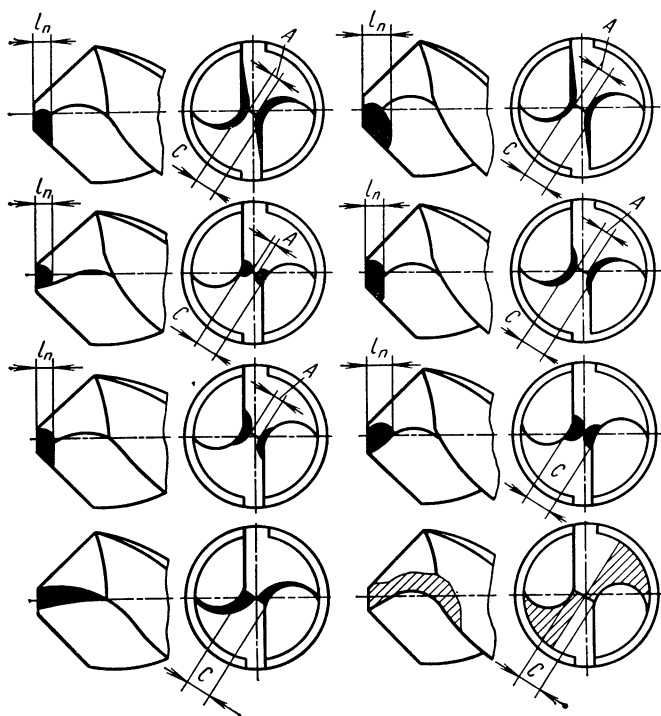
Формы подточки главных и поперечной режущих кромок сверла:
